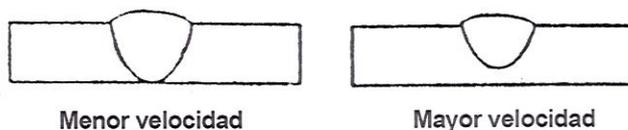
Efecto de la velocidad de soldadura sobre el perfil de cordón
